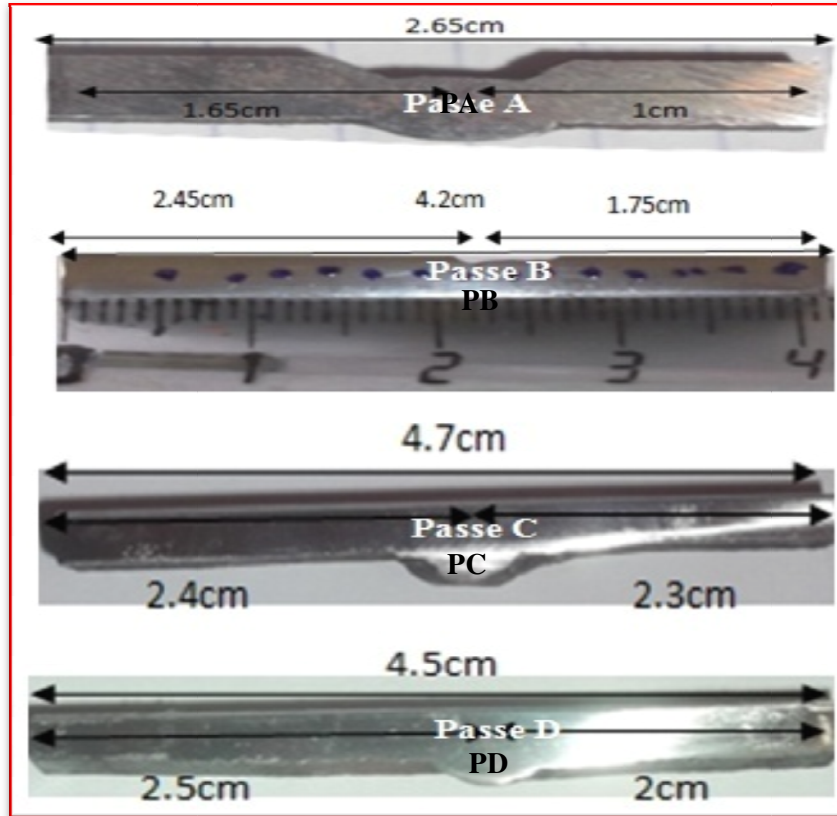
Macrographies en première passe de soudage (PA, PB, PC et PD).
